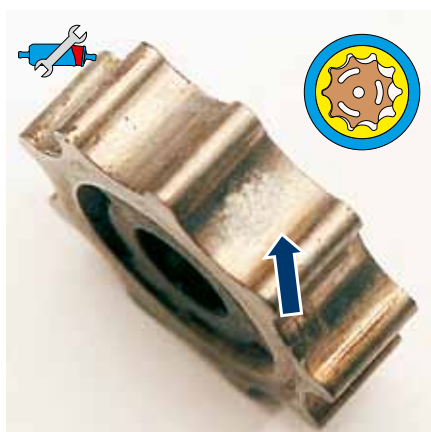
Трохоидное зубчатое колесо с известковыми отложениями
